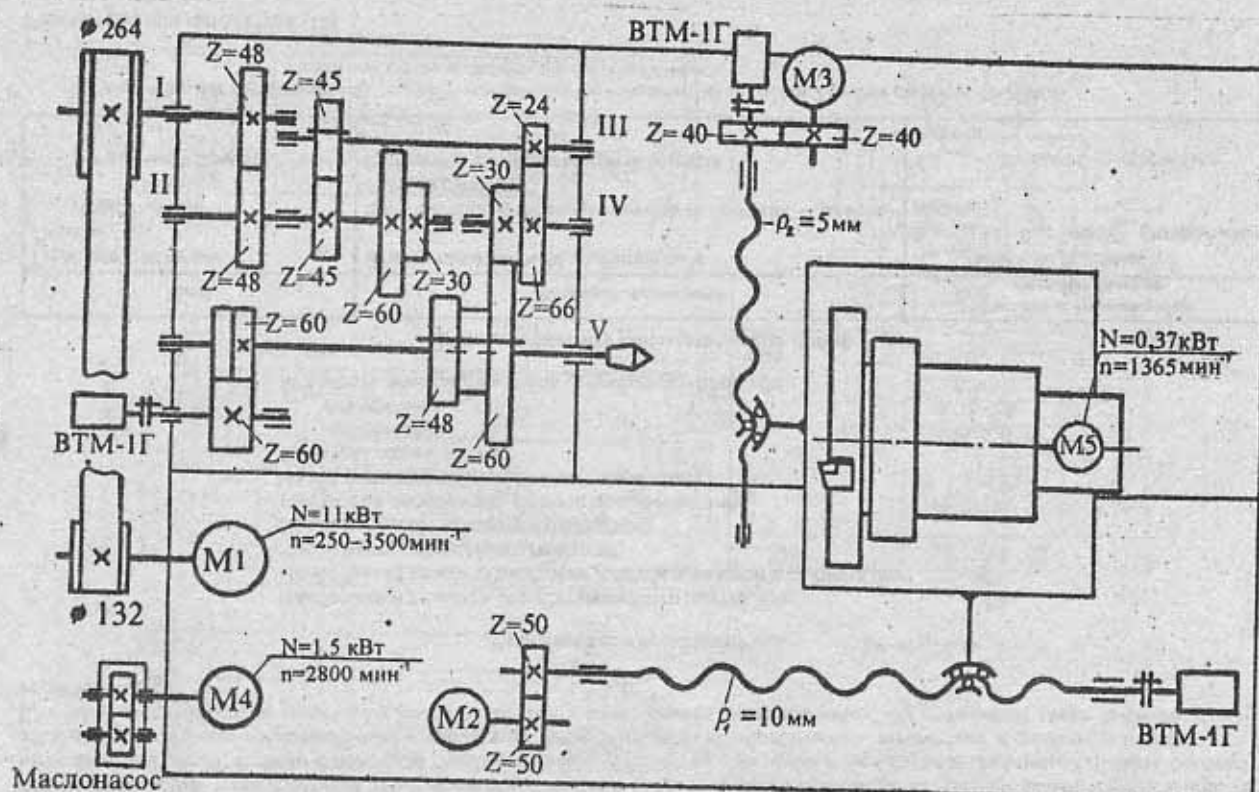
Кинематическая схема токарного станка мод. 16К20РФ3С19 с ЧПУ
